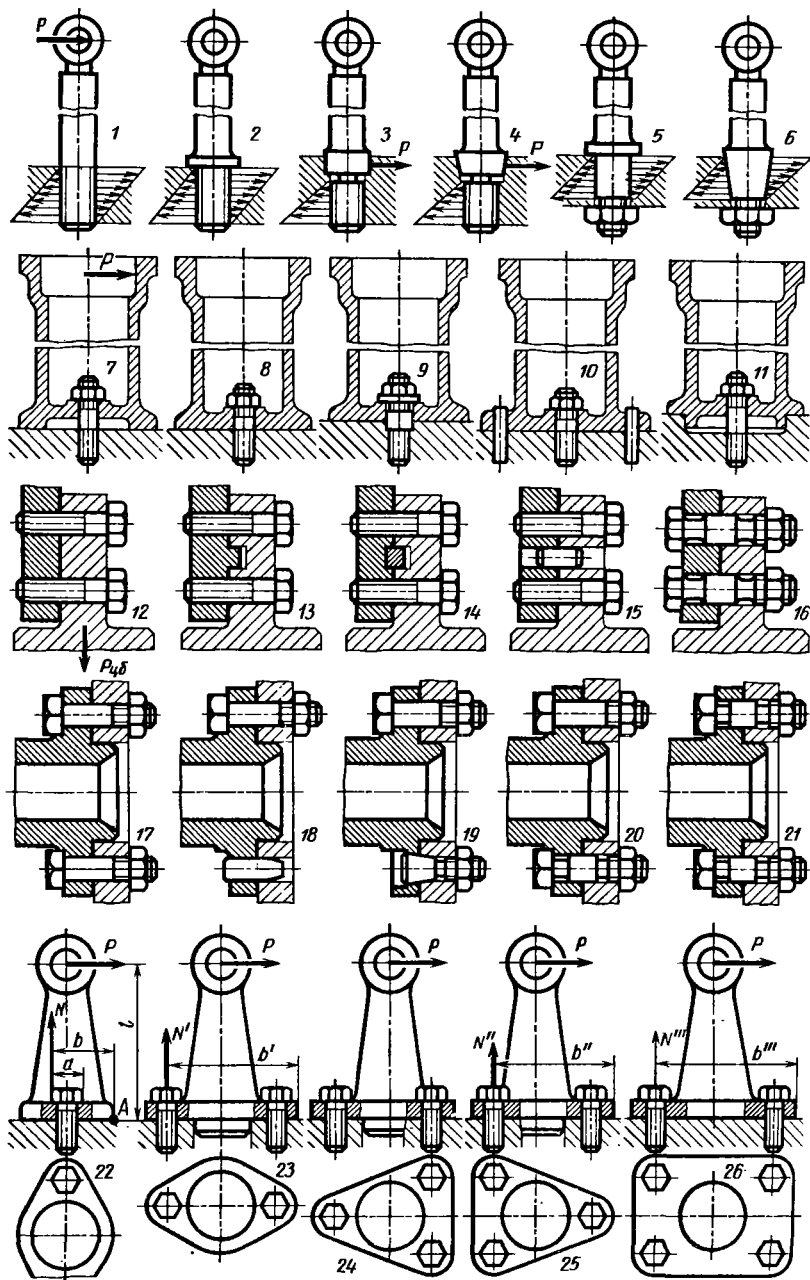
Разгрузка резьбовых деталей от изгиба и среза
